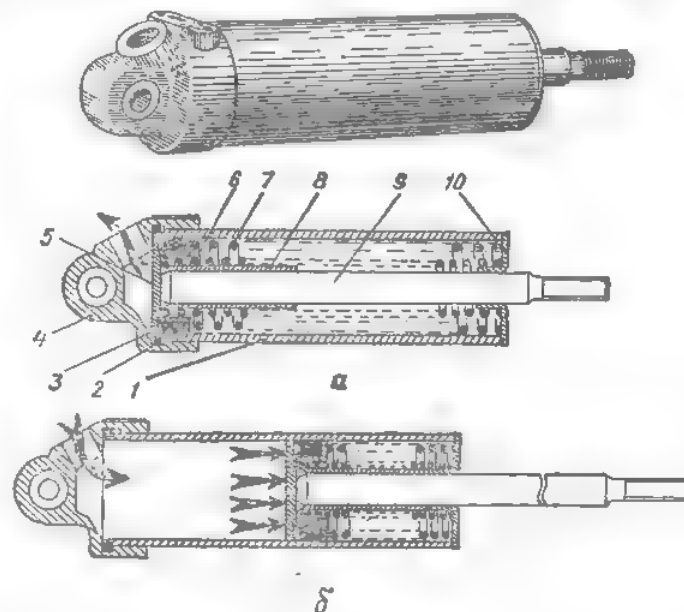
Пневматический цилиндр вспомогательного тормоза:
